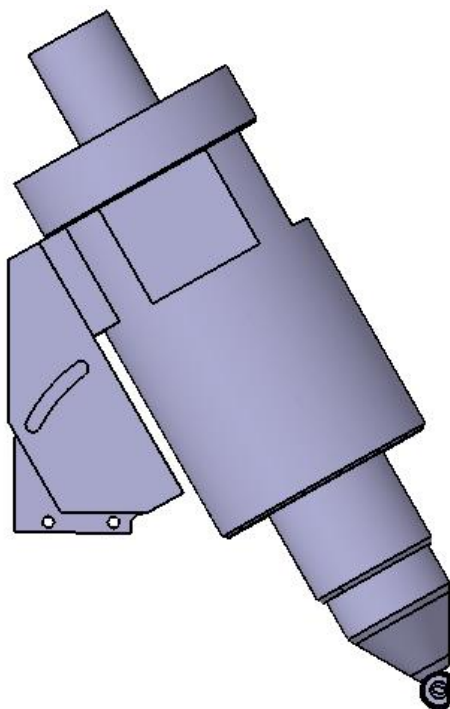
Rekonstruirani CAD model izvora zračenja – dimenzije glavnih značajki [9]
